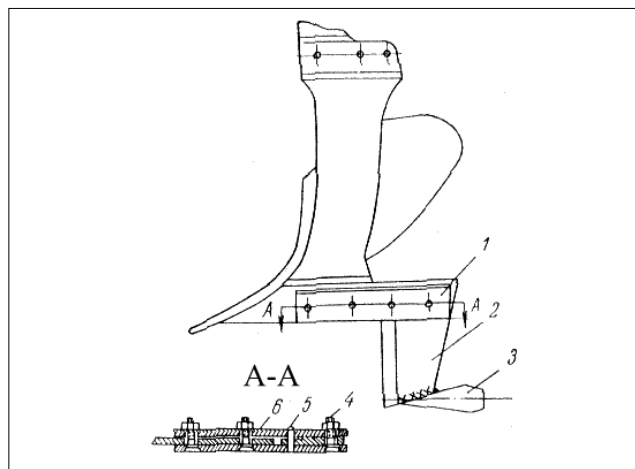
Кротователь, соединенный с корпусом плуга: 1 – полевая доска; 2 – нож; 3 – дренаж; 4 – болты; 5 – предохранительная шпилька; 6 – планка
